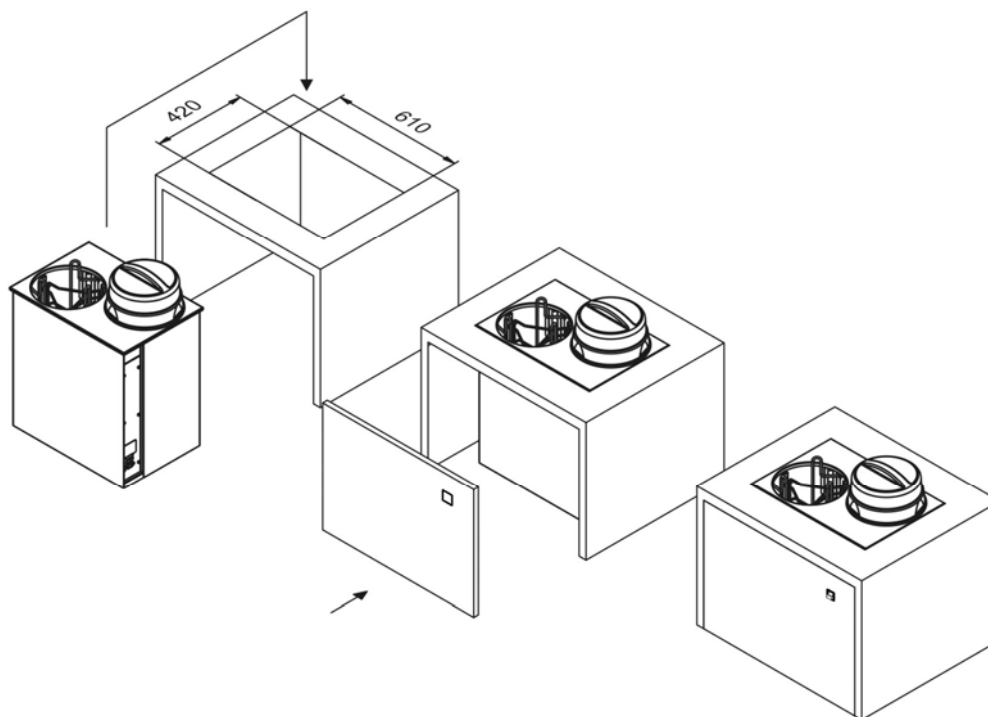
Instrucciones de montaje EBRH-2/V19-26
